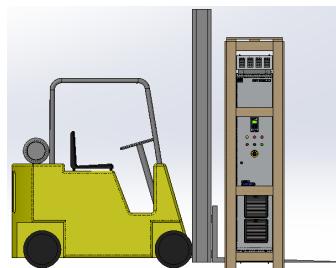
Vista lateral de la carretilla elevadora bajada
